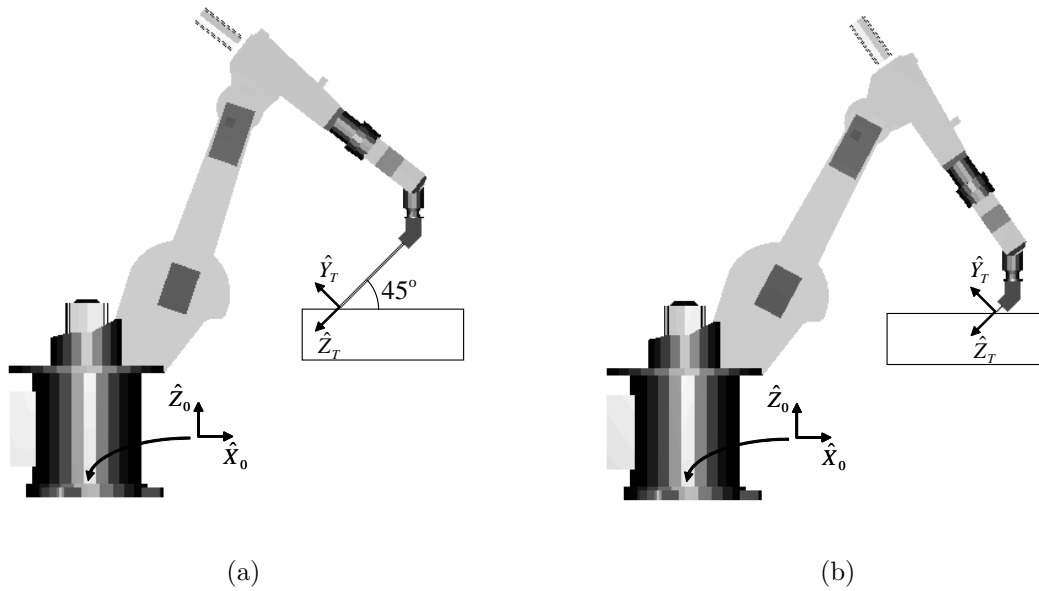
Posições inicial (a) e final (b) do manipulador durante a soldagem com eletrodo revestido para soldagem com ângulo de  $45^\circ$ .
